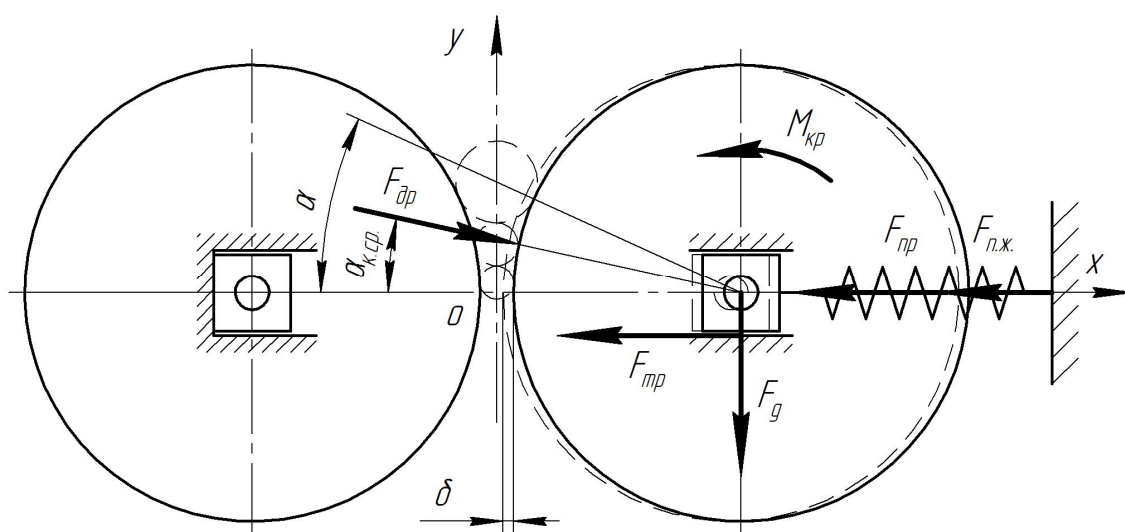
Расчетная схема нагрузок для определения закона перемещений валка валковой дробилки
